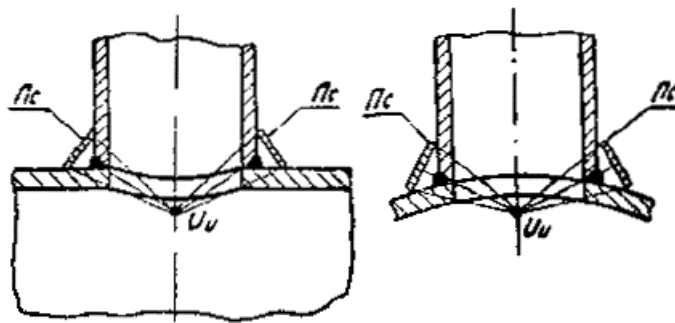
Схема просвечивания криволинейного шва изнутри трубы за одну установку источника излучения
